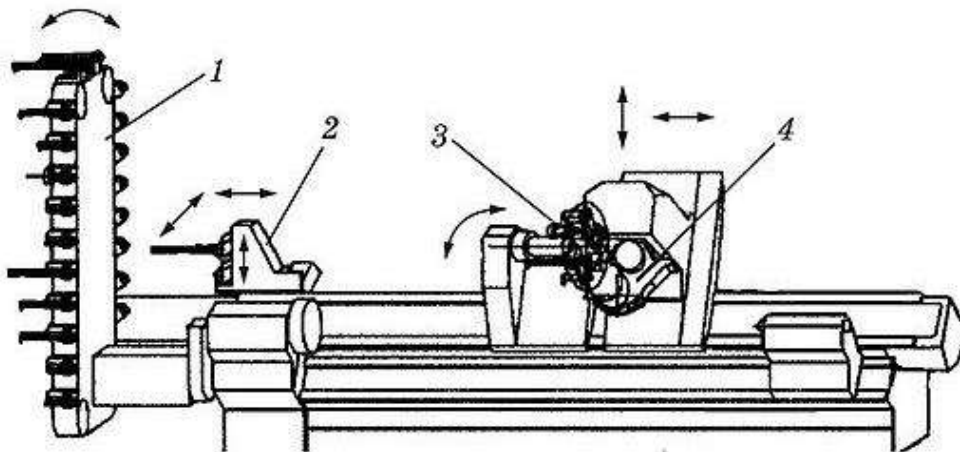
Система зміни інструментів токарного багатопільового верстата HEYNUMAT 35:1 - основний магазин; 2 - лінійний робот-маніпулятор; 3 - проміжний магазин; 4 - інструментальна головка [14]
